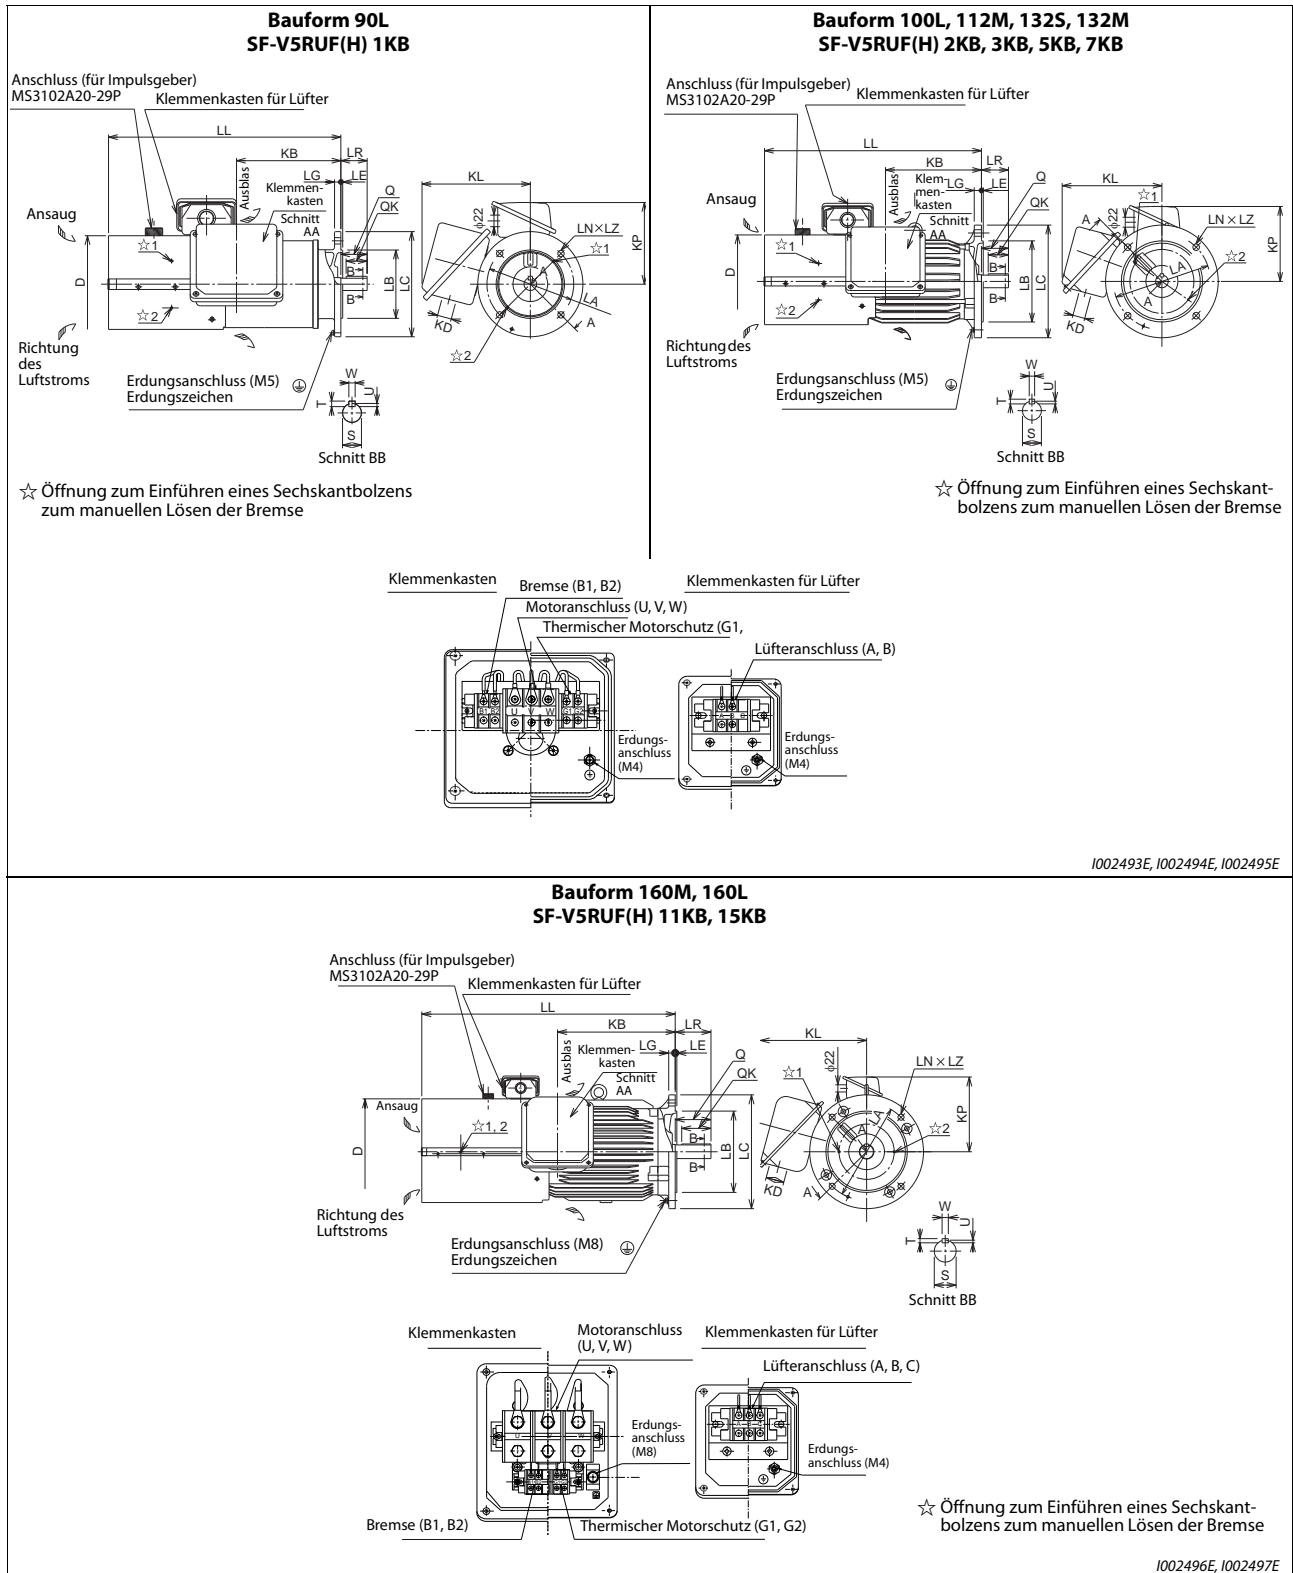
Maßzeichnungen der Motoren SF-V5RUF(H) (mit Befestigungsflansch und Bremse)
